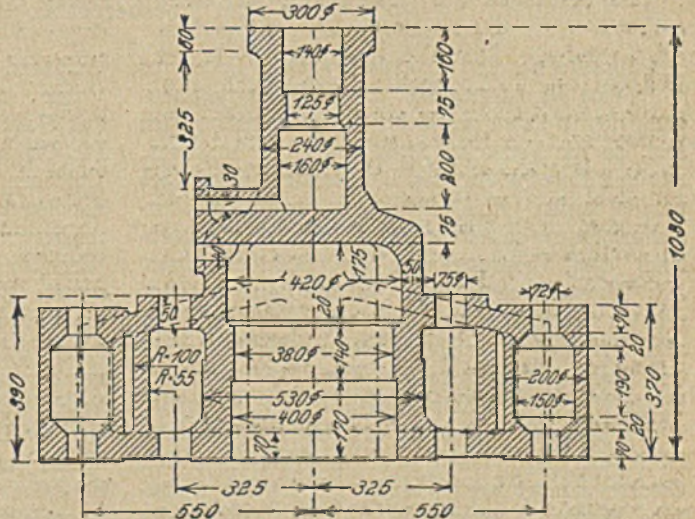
Unvorteilhaft konstruierter Preßzylinder.
